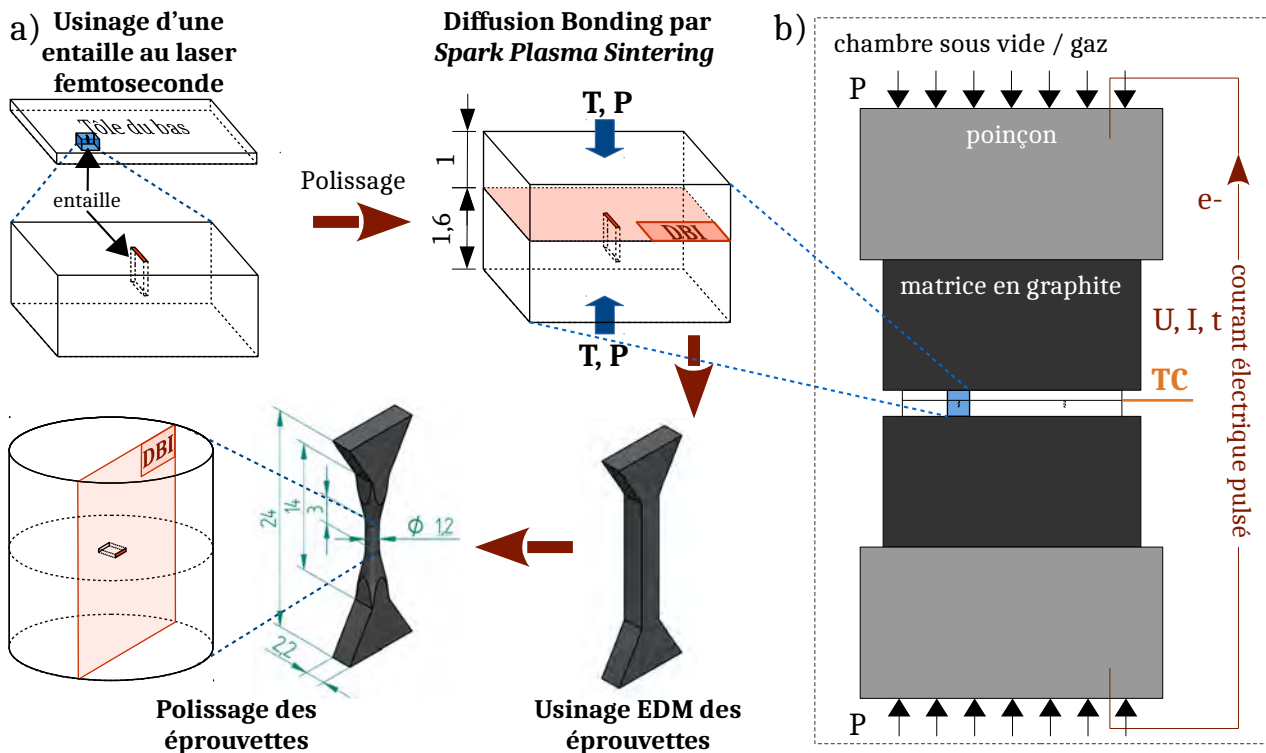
a) Principe de fabrication des éprouvettes de fatigue à défaut interne centré. b) Schéma simplifié du soudage par diffusion des éprouvettes au SPS.
